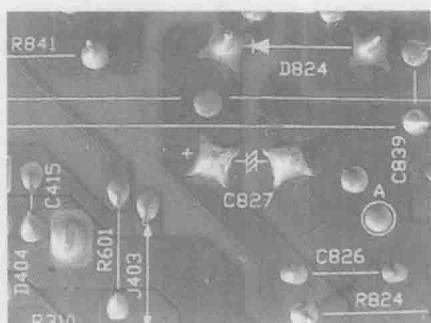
PCB 实现元器件的布线、电气连接、电绝缘
